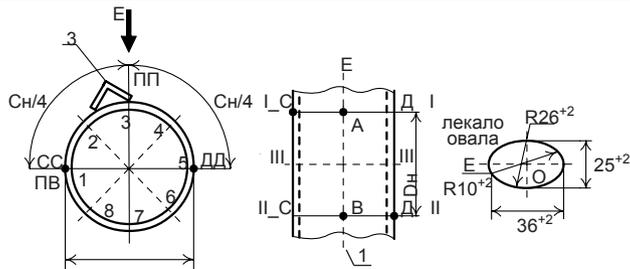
Разметка трубопровода для приварки держателей ПЭП
